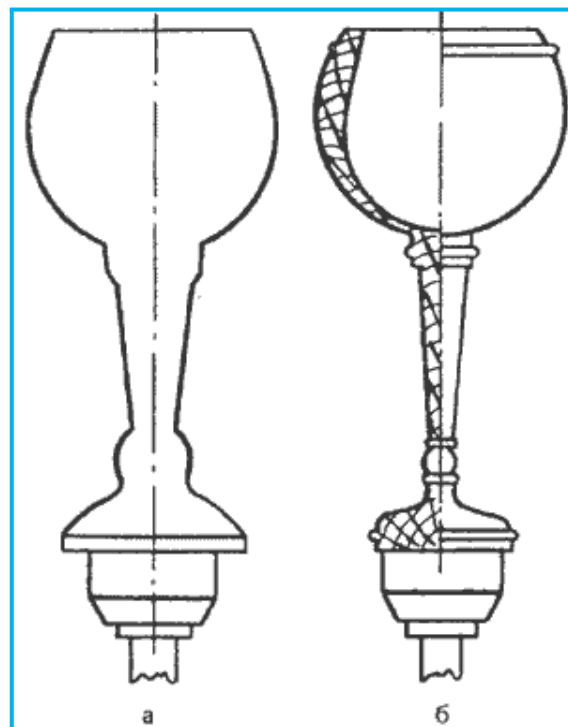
1. Точіння кубка: а — загальний вигляд, б — розріз
